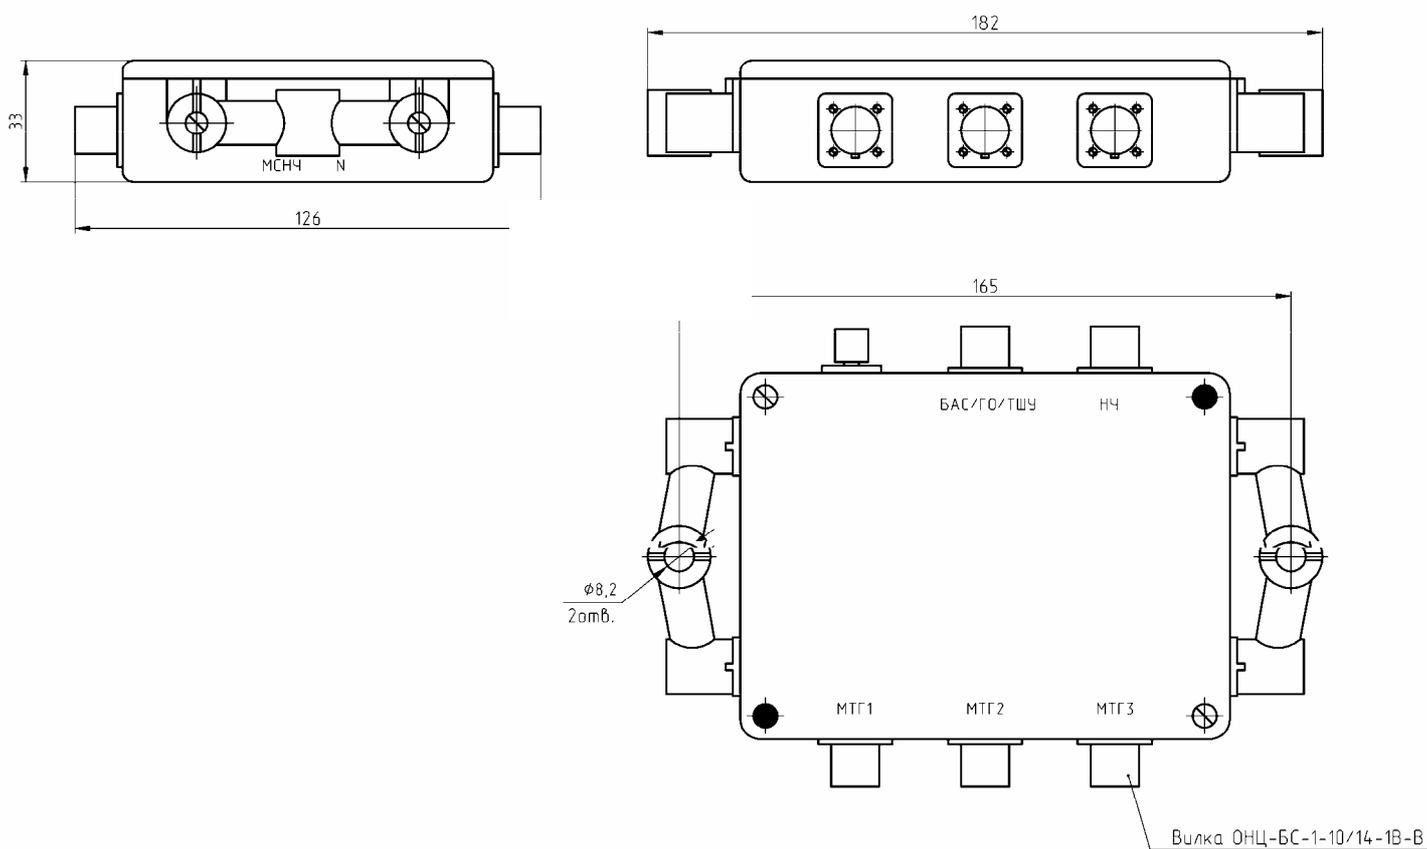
Габаритные чертежи блока сопряжения МСНЧ
